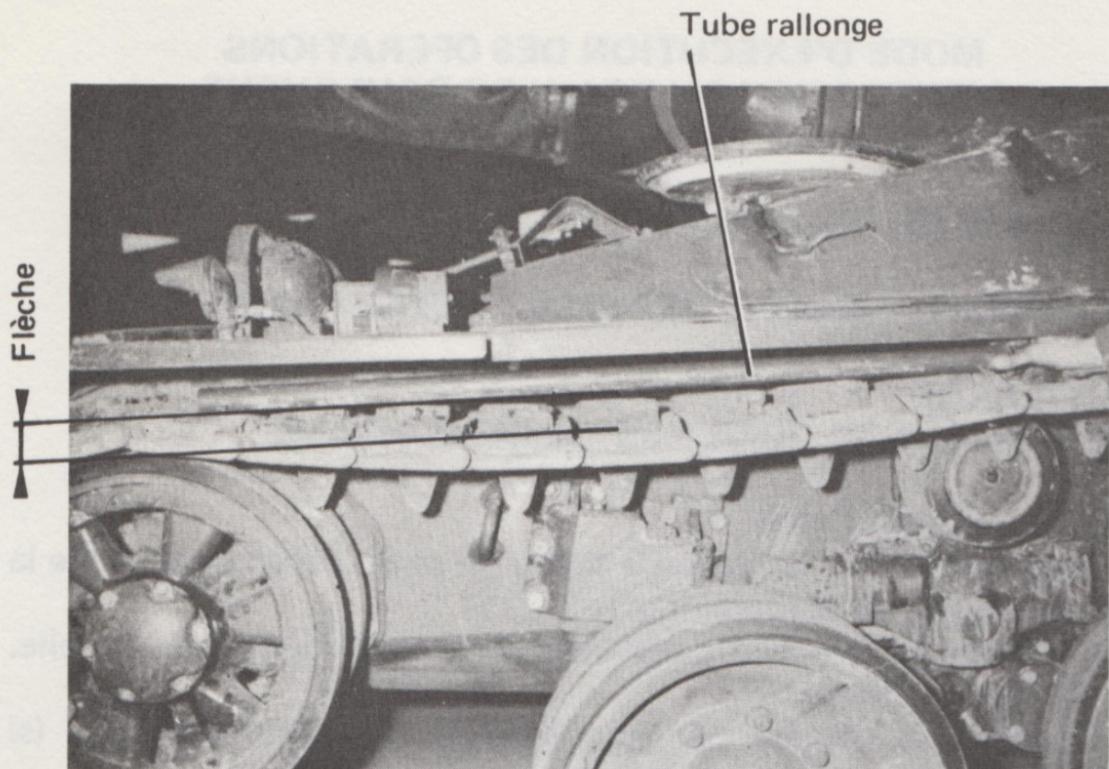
TENSION DE LA CHENILLE (chenille à tendre)
